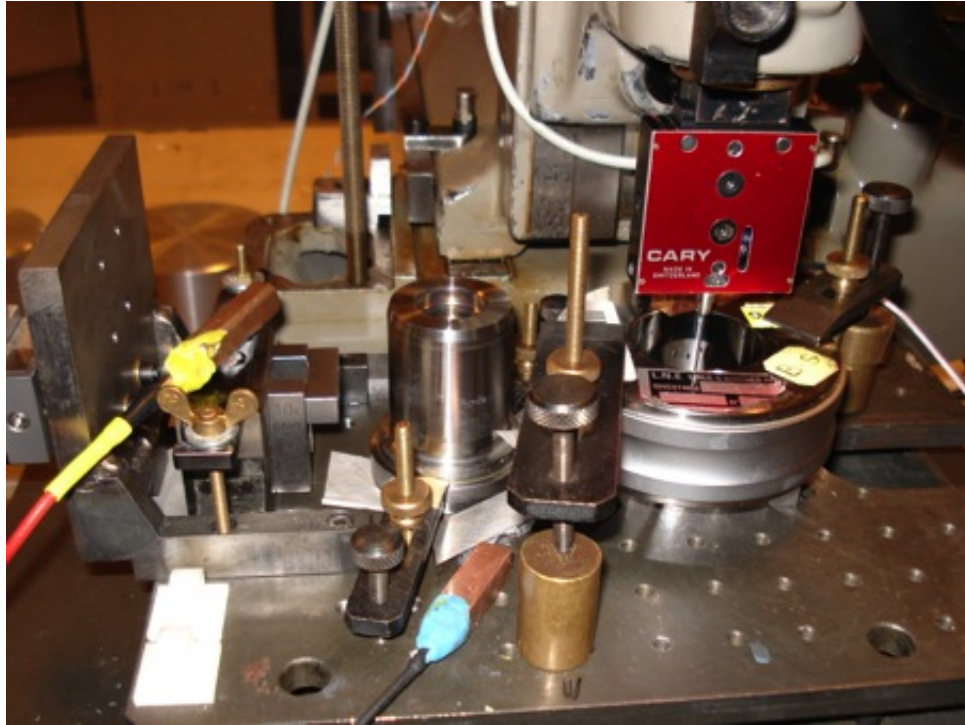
Dispositif d'essai de mesure du diamètre du cylindre pour l'ensemble piston-cylindre
